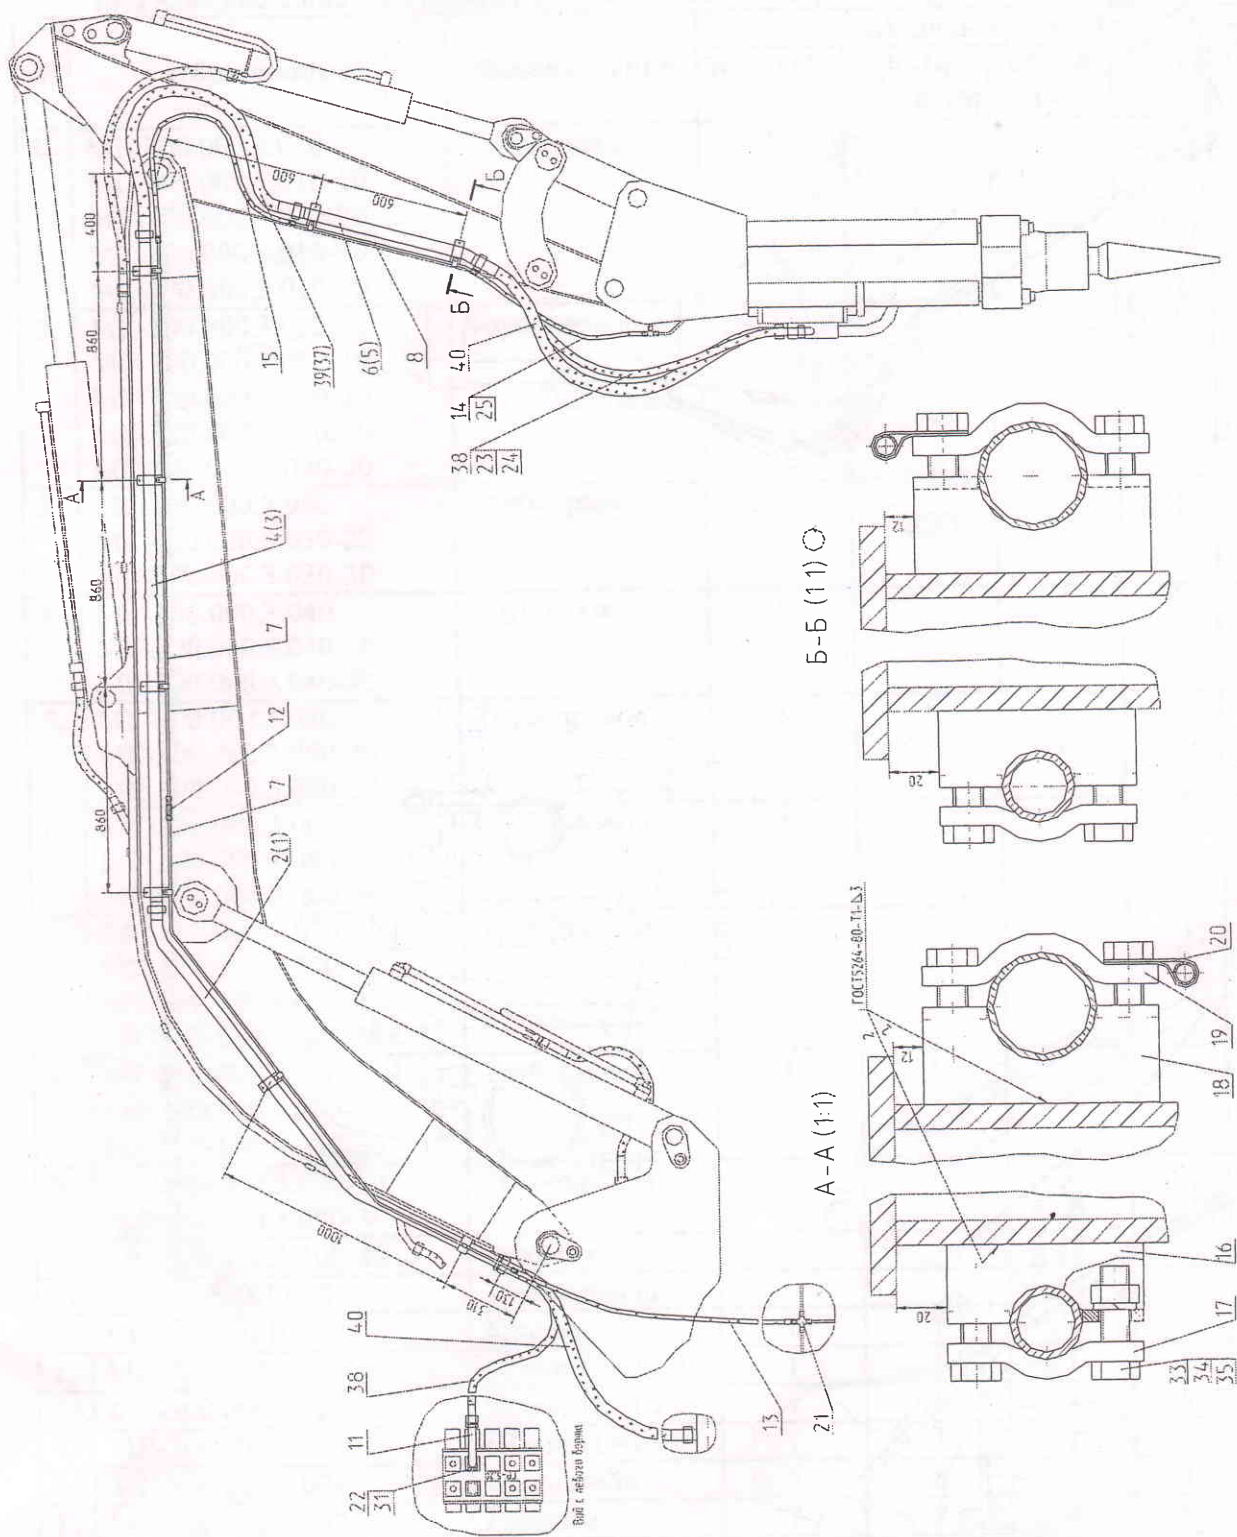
Монтаж гидрооборудования гидромолота на рабочем оборудовании экскаватора ЕК-12
